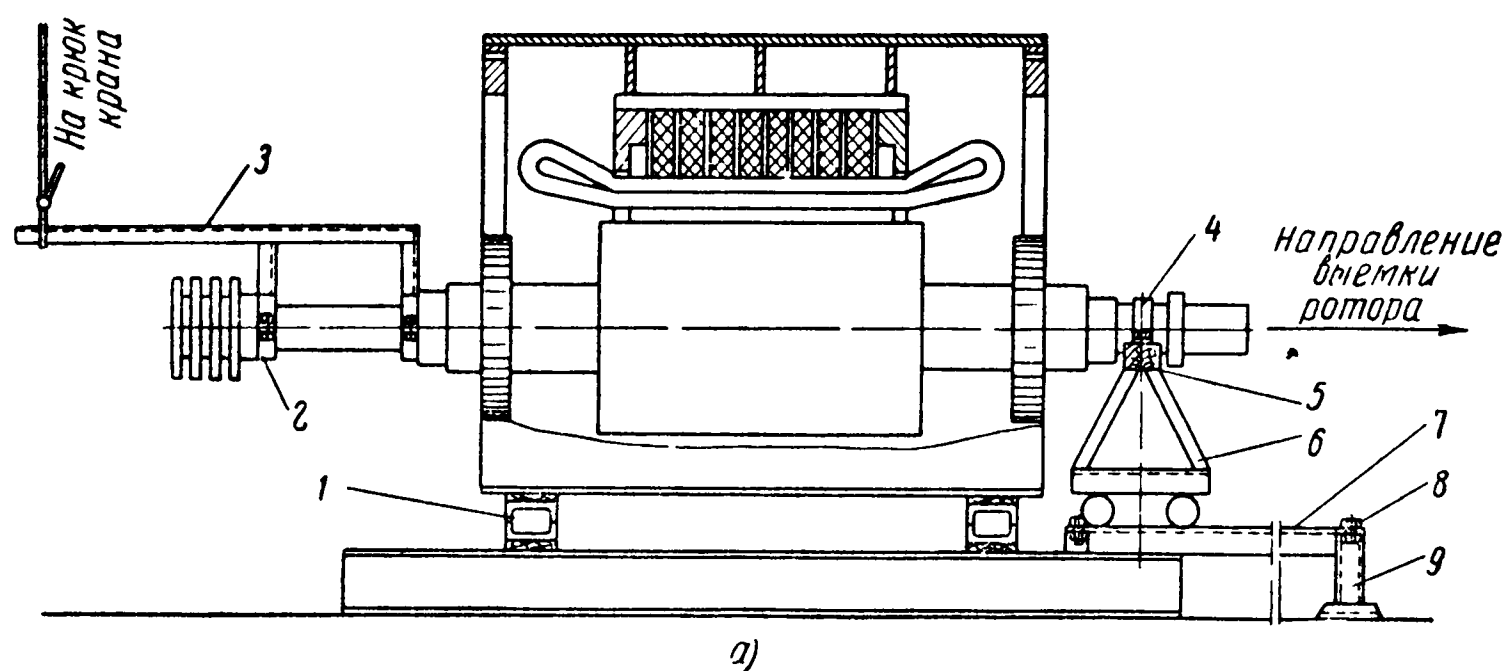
Схема выемки ротора из статора двигателя АТМ-2000:
